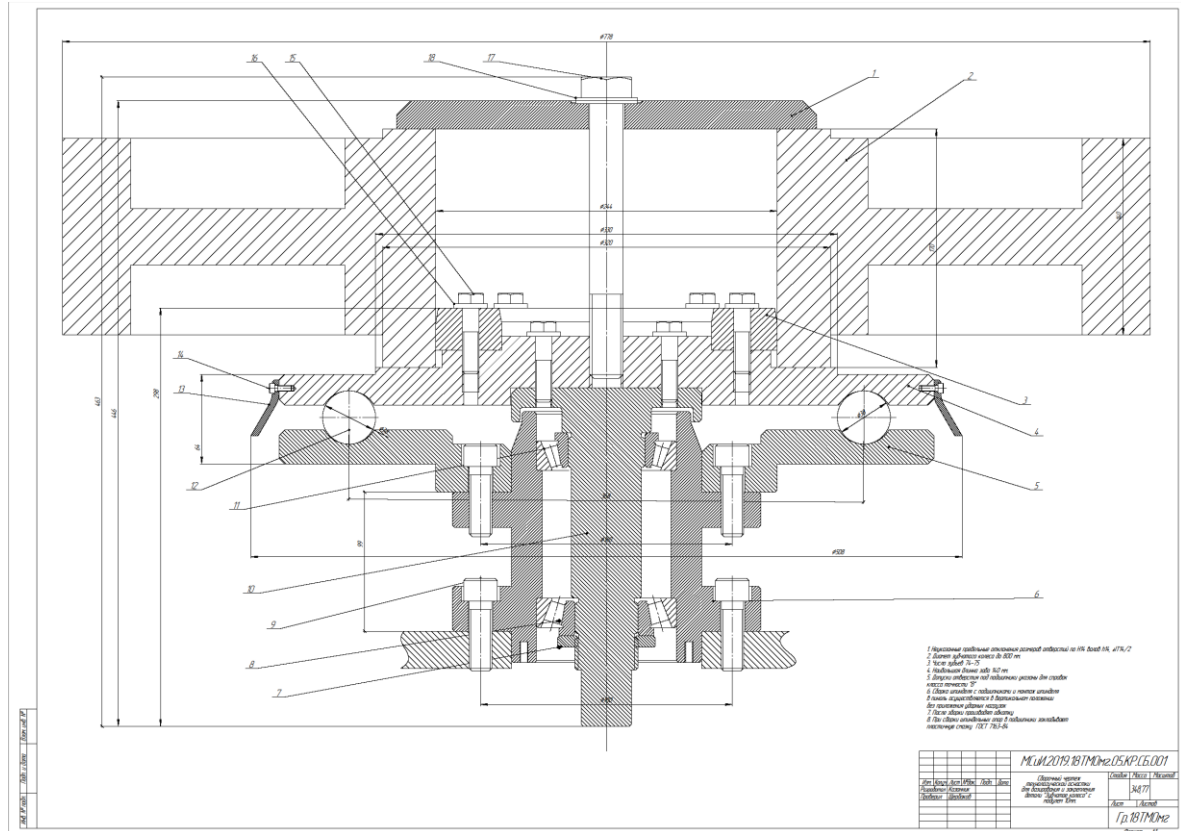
Конструкция шпиндельного узла и схема базирования и закрепления заготовки
